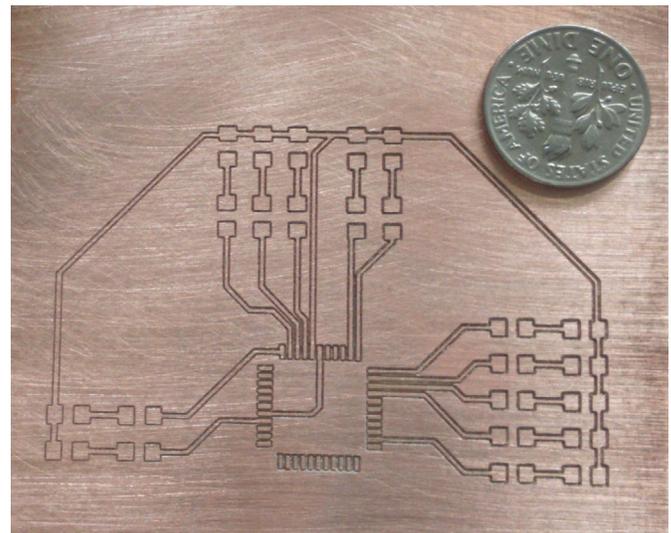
PCB con pistas de 16 mills. de pulgada.
